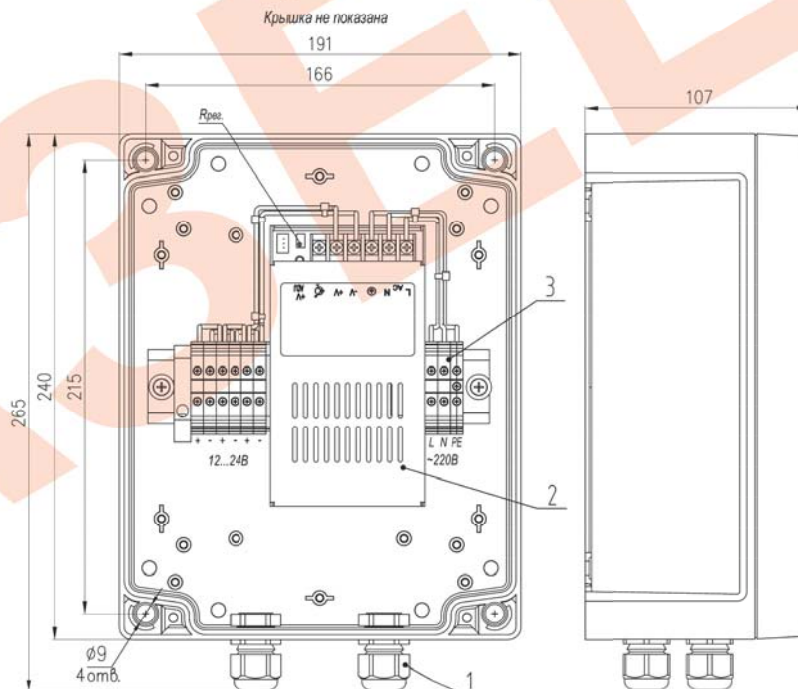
Устройство, габаритные и установочные размеры БПГ-75Вт.
